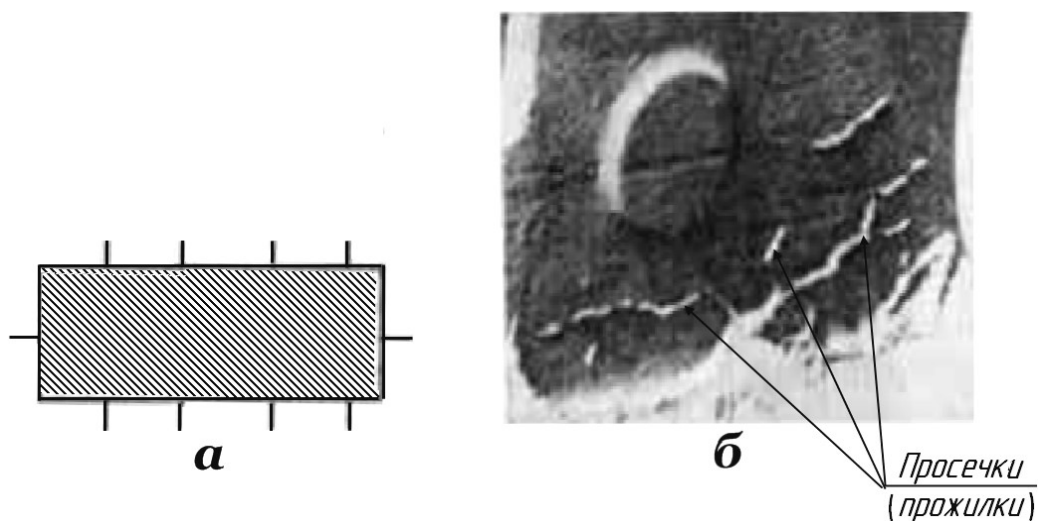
Дефект – просечки (прожилки): а – схема; б – дефектная отливка
